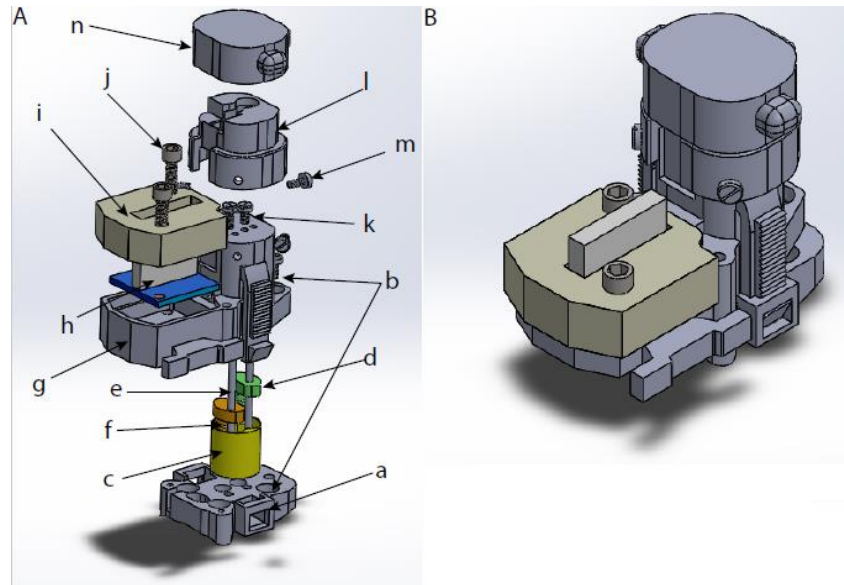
Diseño Final. (A) Vista explosiva. (B) Vista Isométrica.
